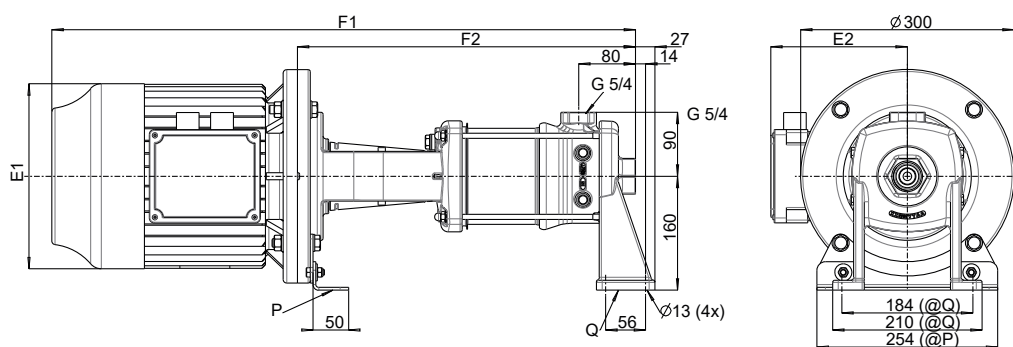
Abmessungen und Anschlüsse Movitec H(S)I 6 mit Motor V1
